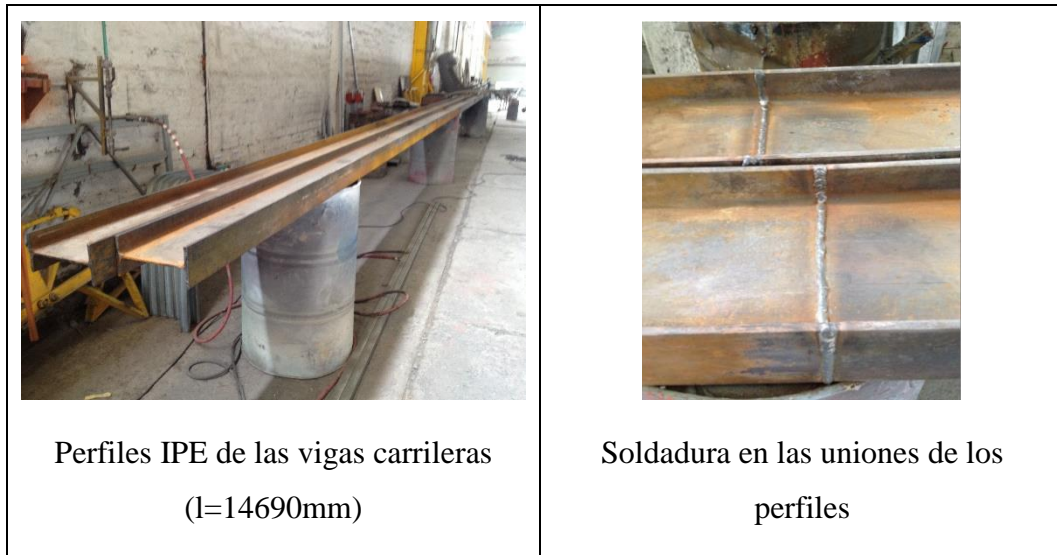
Soldadura en las uniones de los perfiles IPE de las vigas carrileras
